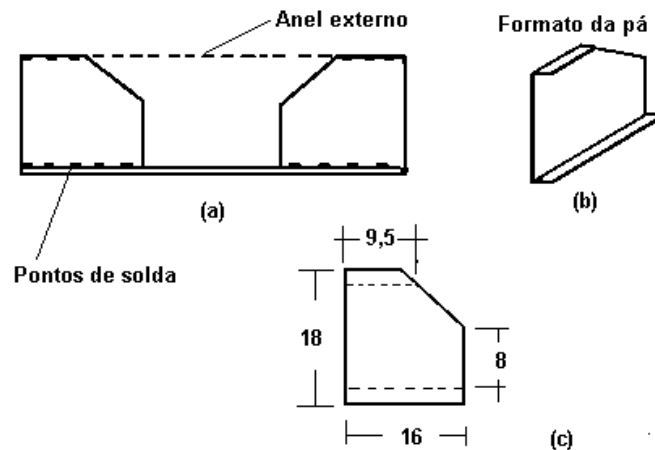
Dimensões, detalhes e posicionamentos das pás no disco principal.
